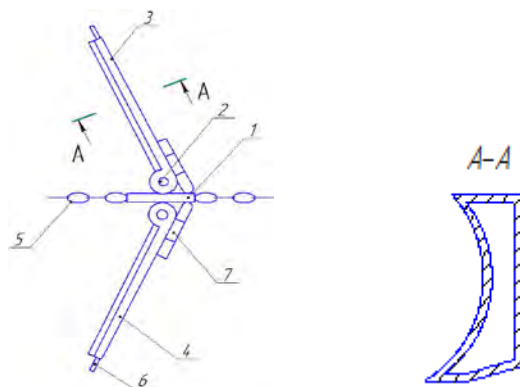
Розроблений скреперний пристрій для прибирання гною
